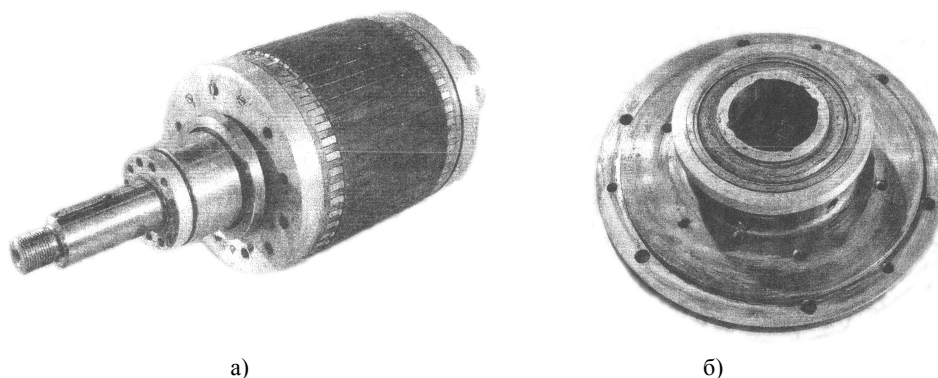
Элементы двигателя АМВ-5: а – ротор с подвижными втулками из стали ДИ48-ВД и протекторными дисками; б – подшипниковый щит с вкладышем из металлокерамики и протекторным кольцом
